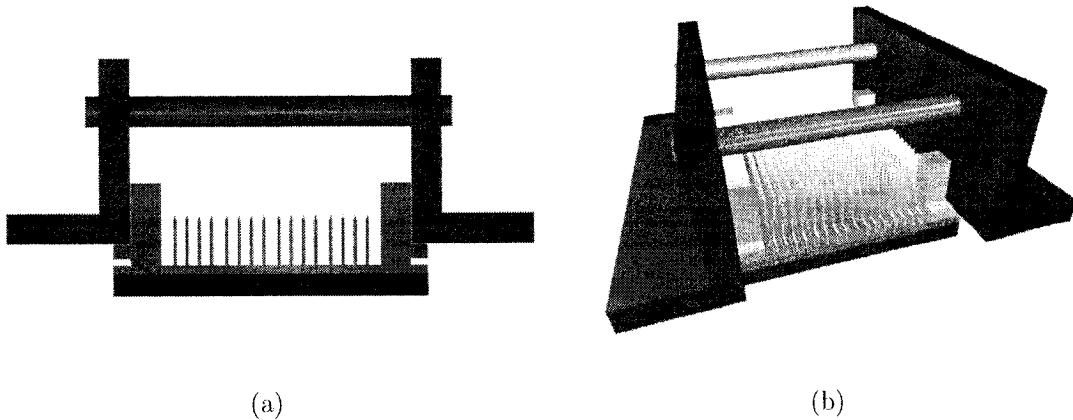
Étau pour sablage du socle. a) Vue de face et b) vue en 3D
